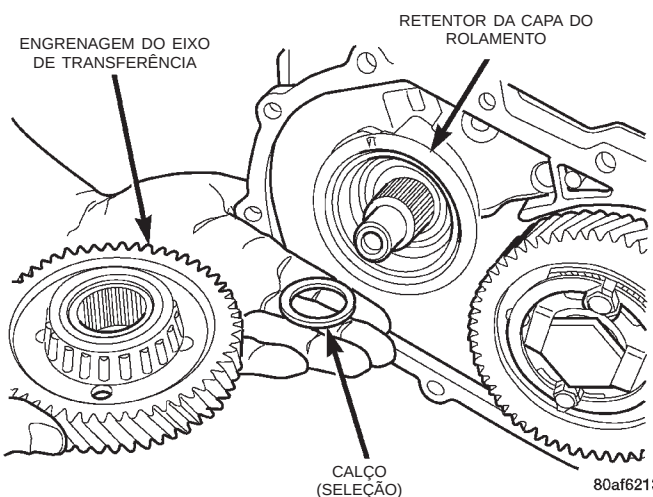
Remoção da Engrenagem do Eixo de Transferência e do Calço (Seleção)
